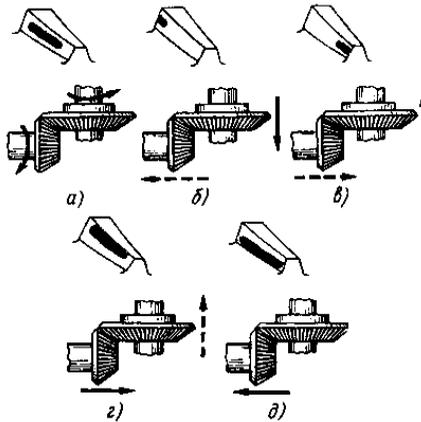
Схемы регулировки (а...д) зацепления конических шестерен главной передачи
